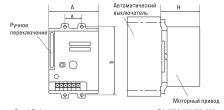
Габаритные размеры моторного привода к ВА-99М 400, 630, 800
